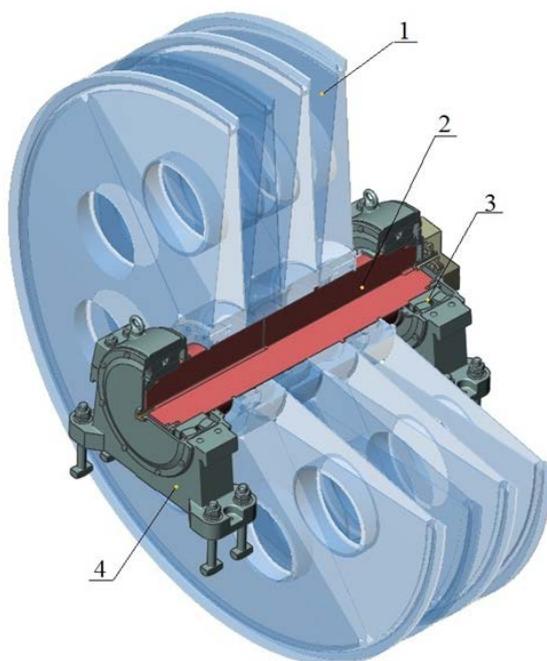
Компьютерная модель узла главного вала в сборе
